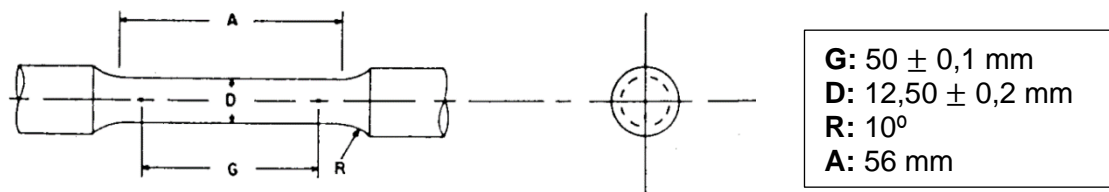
Dimensões para corpo de prova destinada ao ensaio de tração. Fonte: [62].
